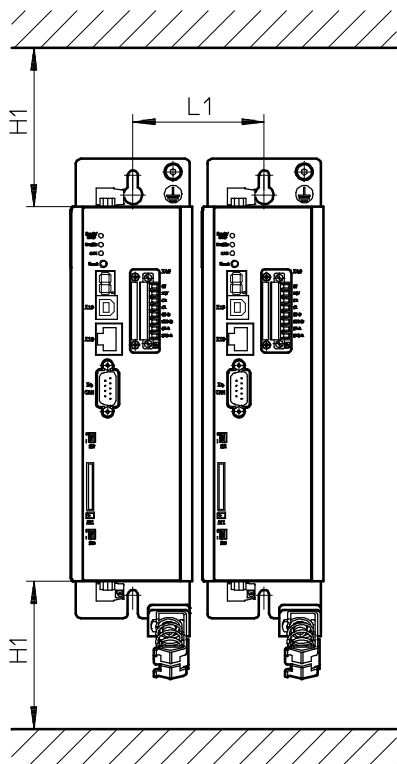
Controlador de motor CMMP-AS-...-M0: Distancia de montaje y espacio para el montaje
